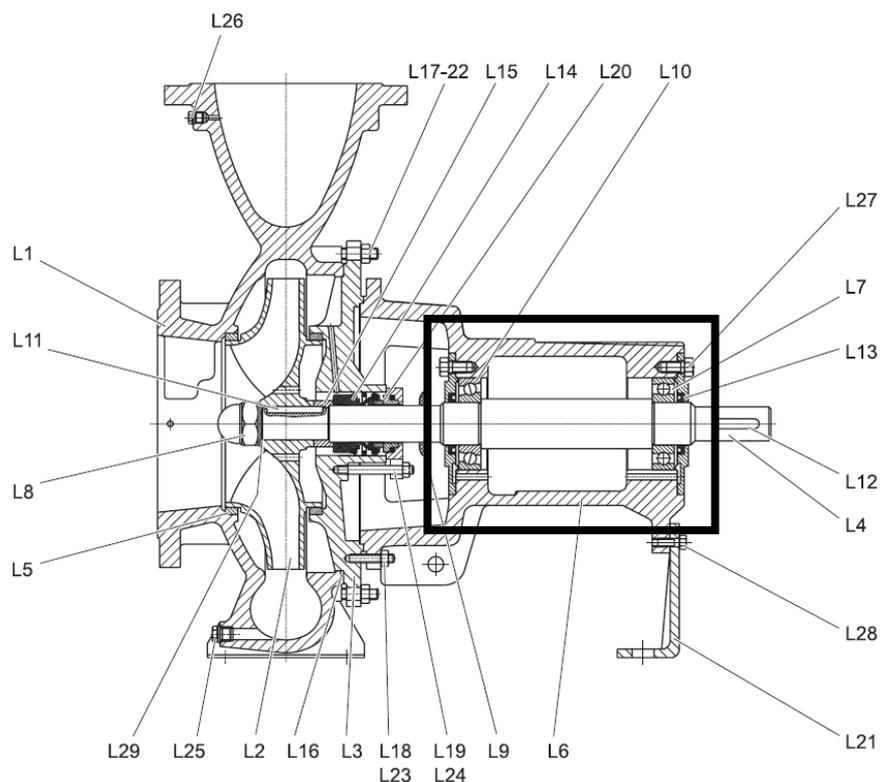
Lagerungsvariante 1 und 2 am Beispiel einer einstufigen Niederdruckpumpe
